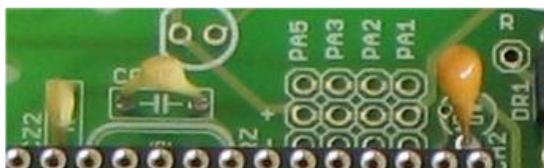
Montagem dos condensadores de 15pF e tantalum.
